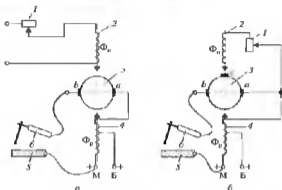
Схема генератора с независимым возбуждением (а) и последовательной размагничивающей обмоткой (б): 1 — реостат; 2 — намагничивающая обмотка; 3 — якорь генератора; 4 — размагничивающая обмотка; 5 — свариваемая заготовка; б — электроподдержатель; Б — большой ток; М — малый ток; а, б, с — щетки генератора
